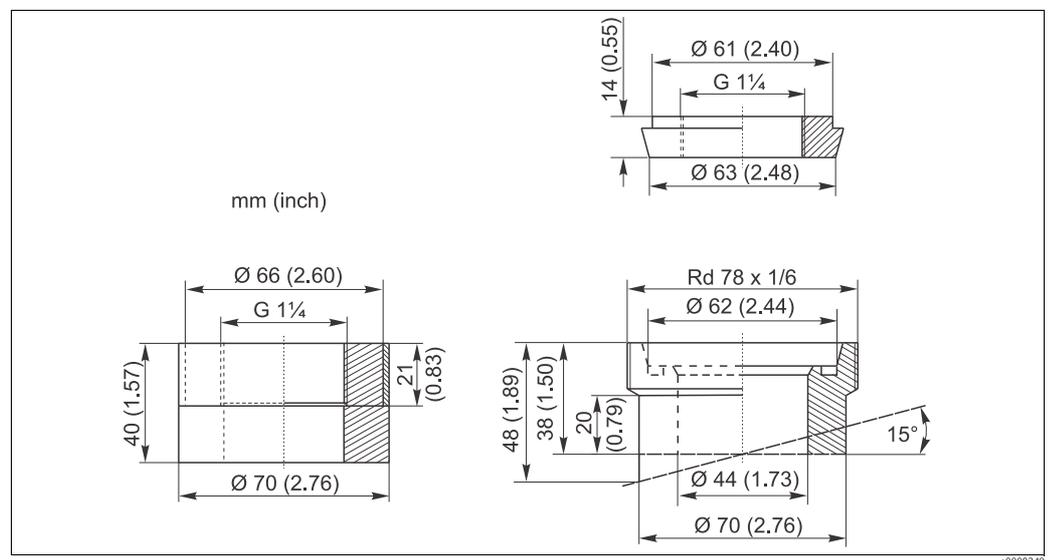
Einschweißstutzen gerade oder schräg
